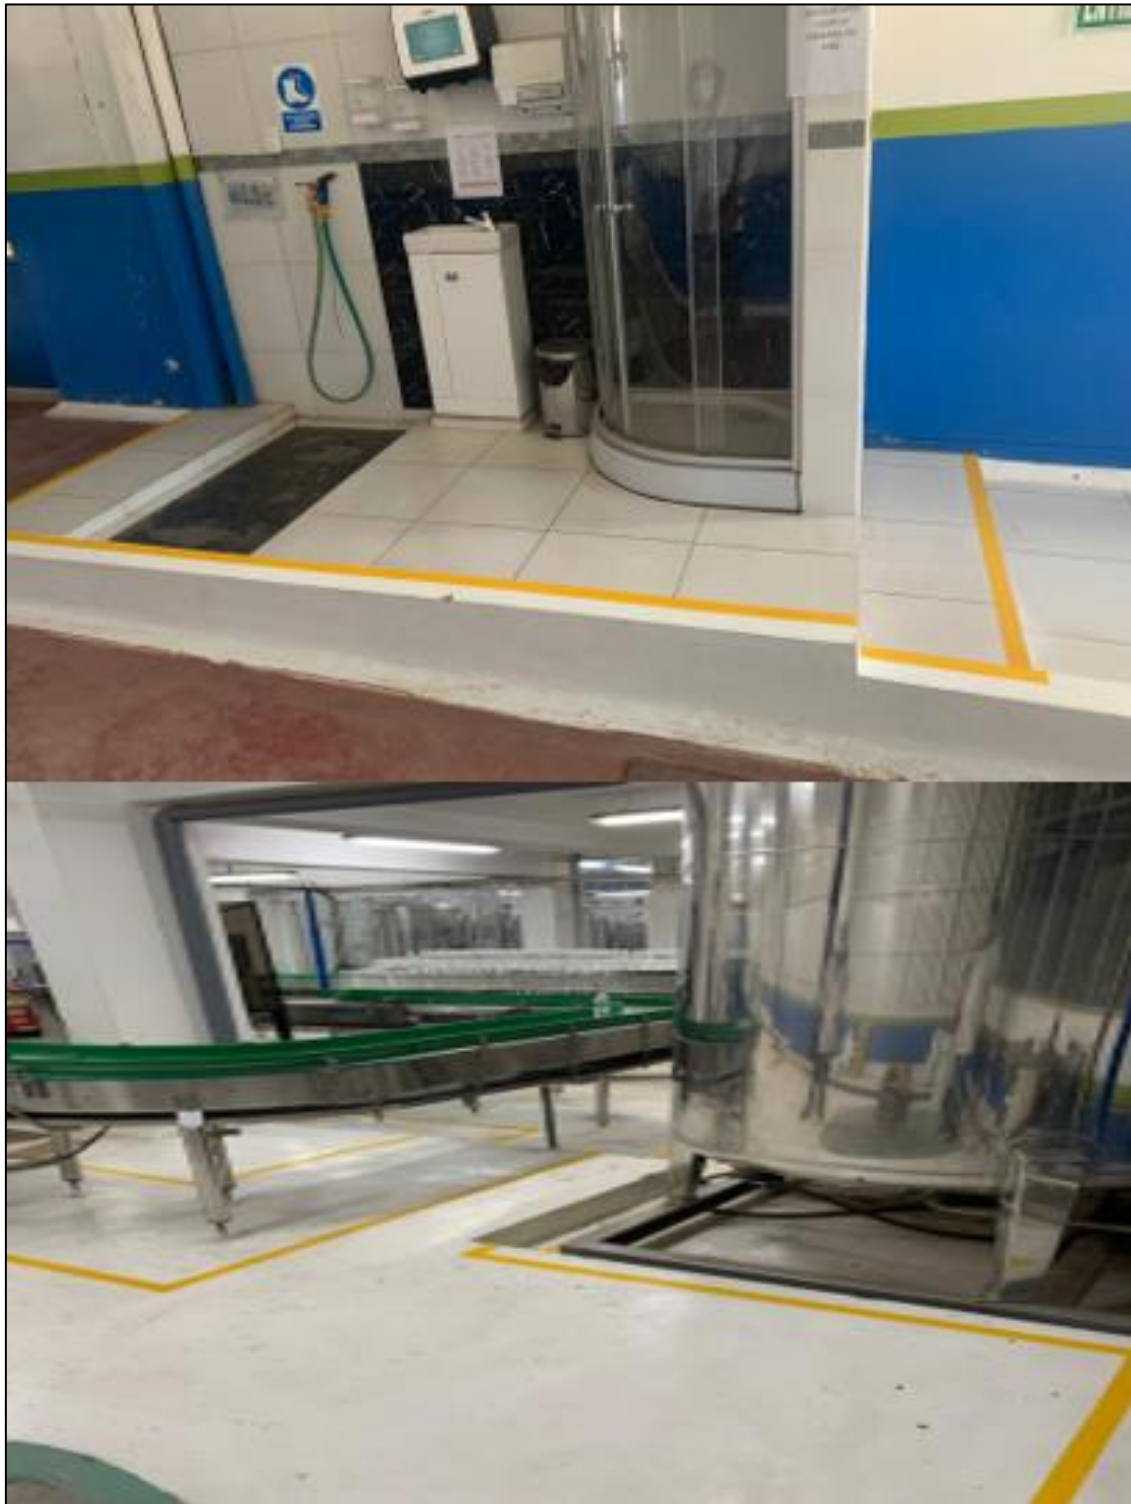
Zona Etiquetado Zegla Tras La Implementación.
